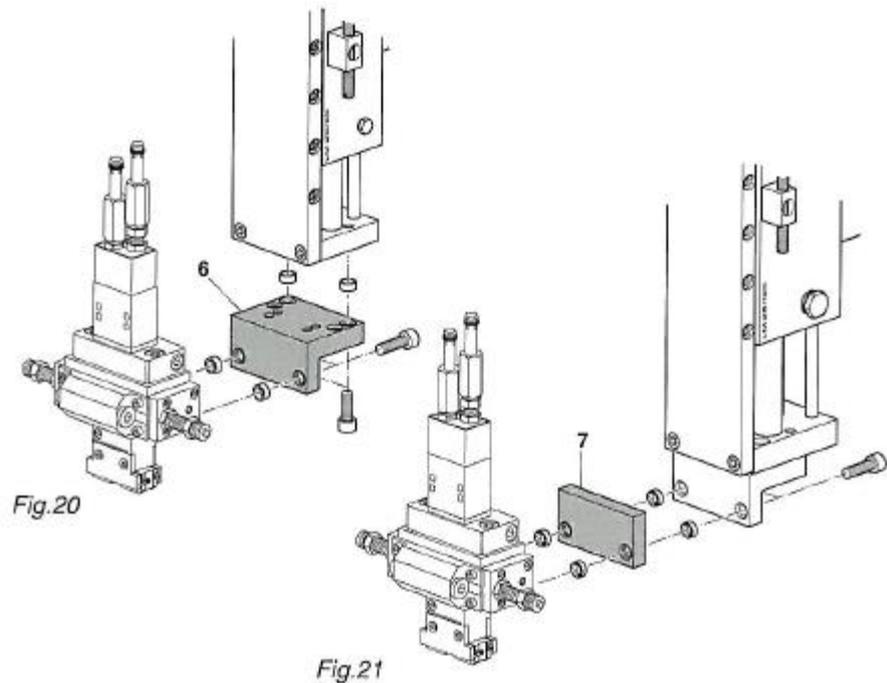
Montage de l'équerre de montage ou de la plaque intermédiaire (LM 25)
